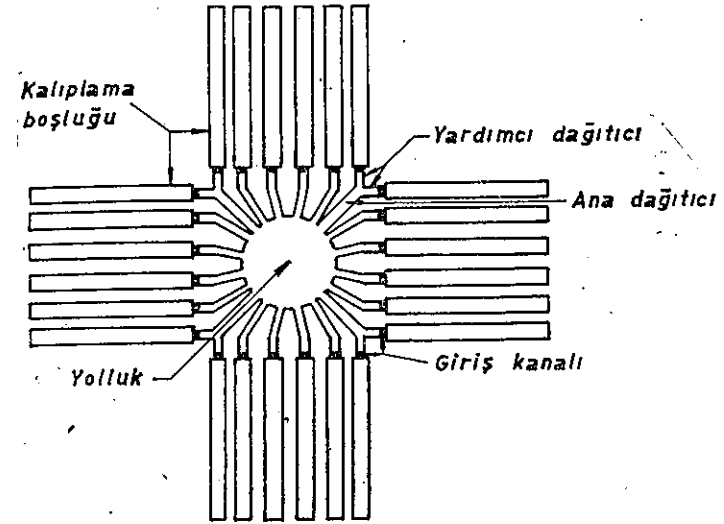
6 Transfer kalıplarında yolluk burcu
